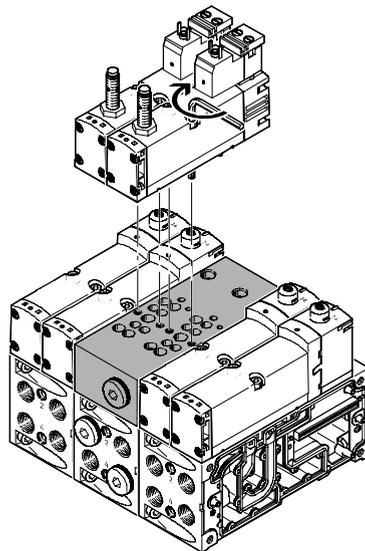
Befestigung der Magnetventile auf dem Steuerblock
